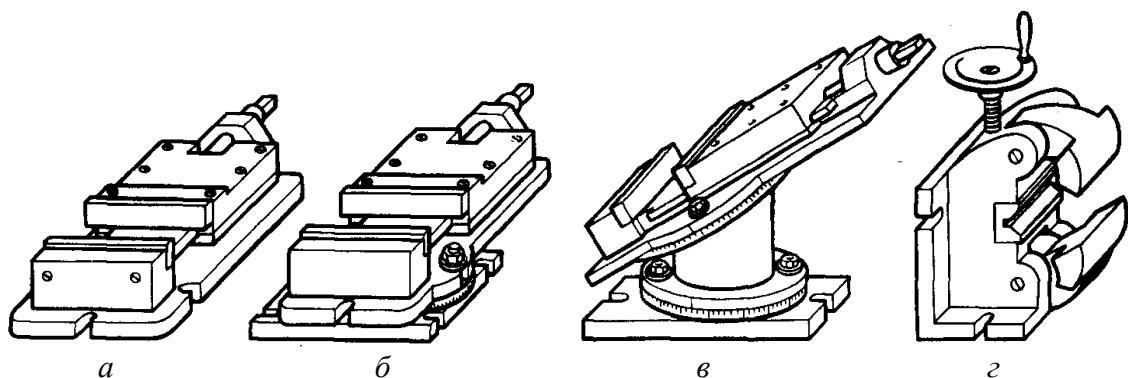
Тиски машинные: а – простые неповоротные; б – поворотные; в – универсальные, позволяющие поворачивать заготовку относительно двух взаимно перпендикулярных осей; г – специальные для закрепления валов;
